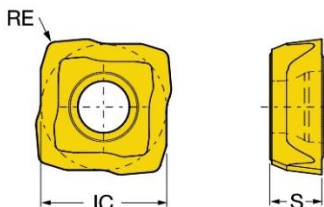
880-06 04 W10H-P-GR 4344 [26].
